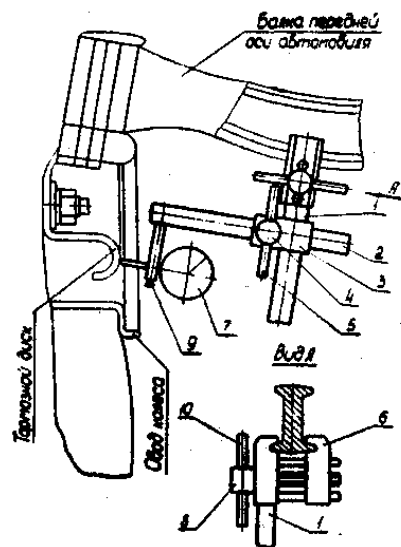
Устройство для проверки радиального зазора в шкворневых соединениях осевого зазора подшипников ступицы переднего колеса:
